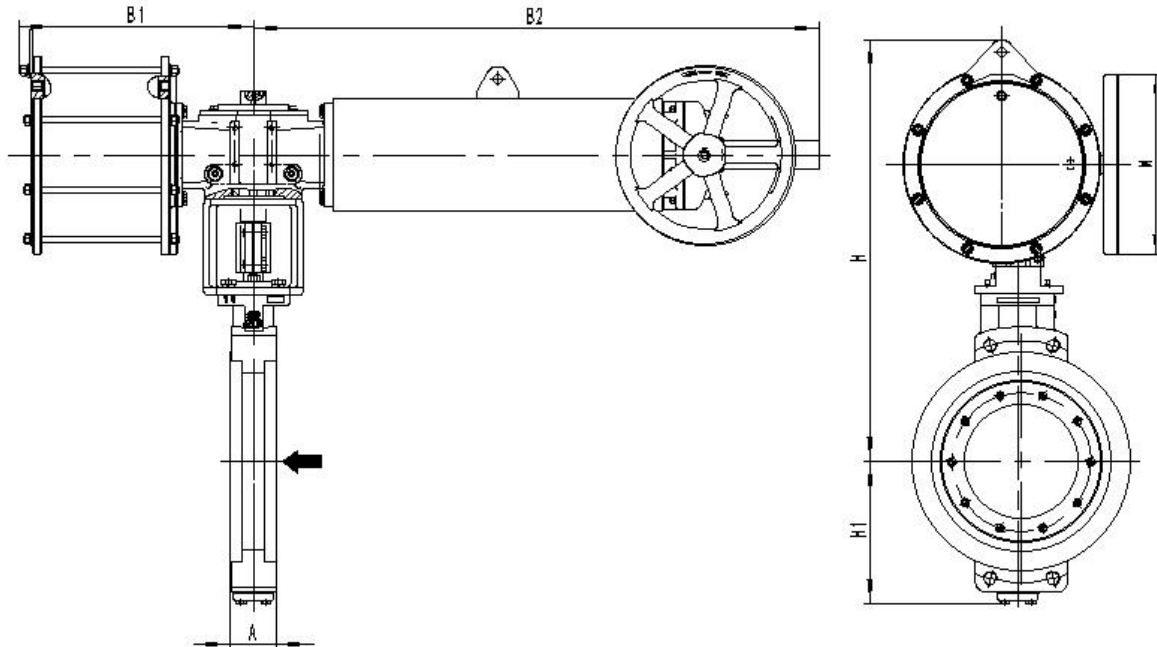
配 AW30SR42~AW40SR53 带伞齿手轮外形尺寸图 (FC)
